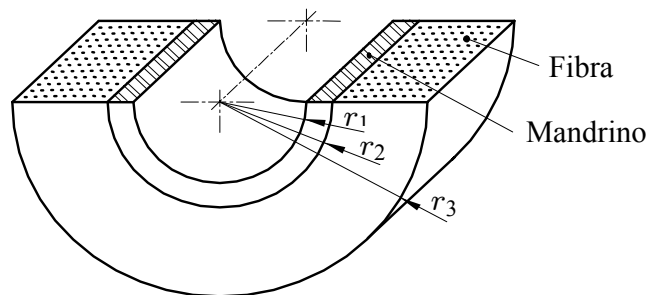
Rotor de fibra con mandrino de bobinado incorporado
